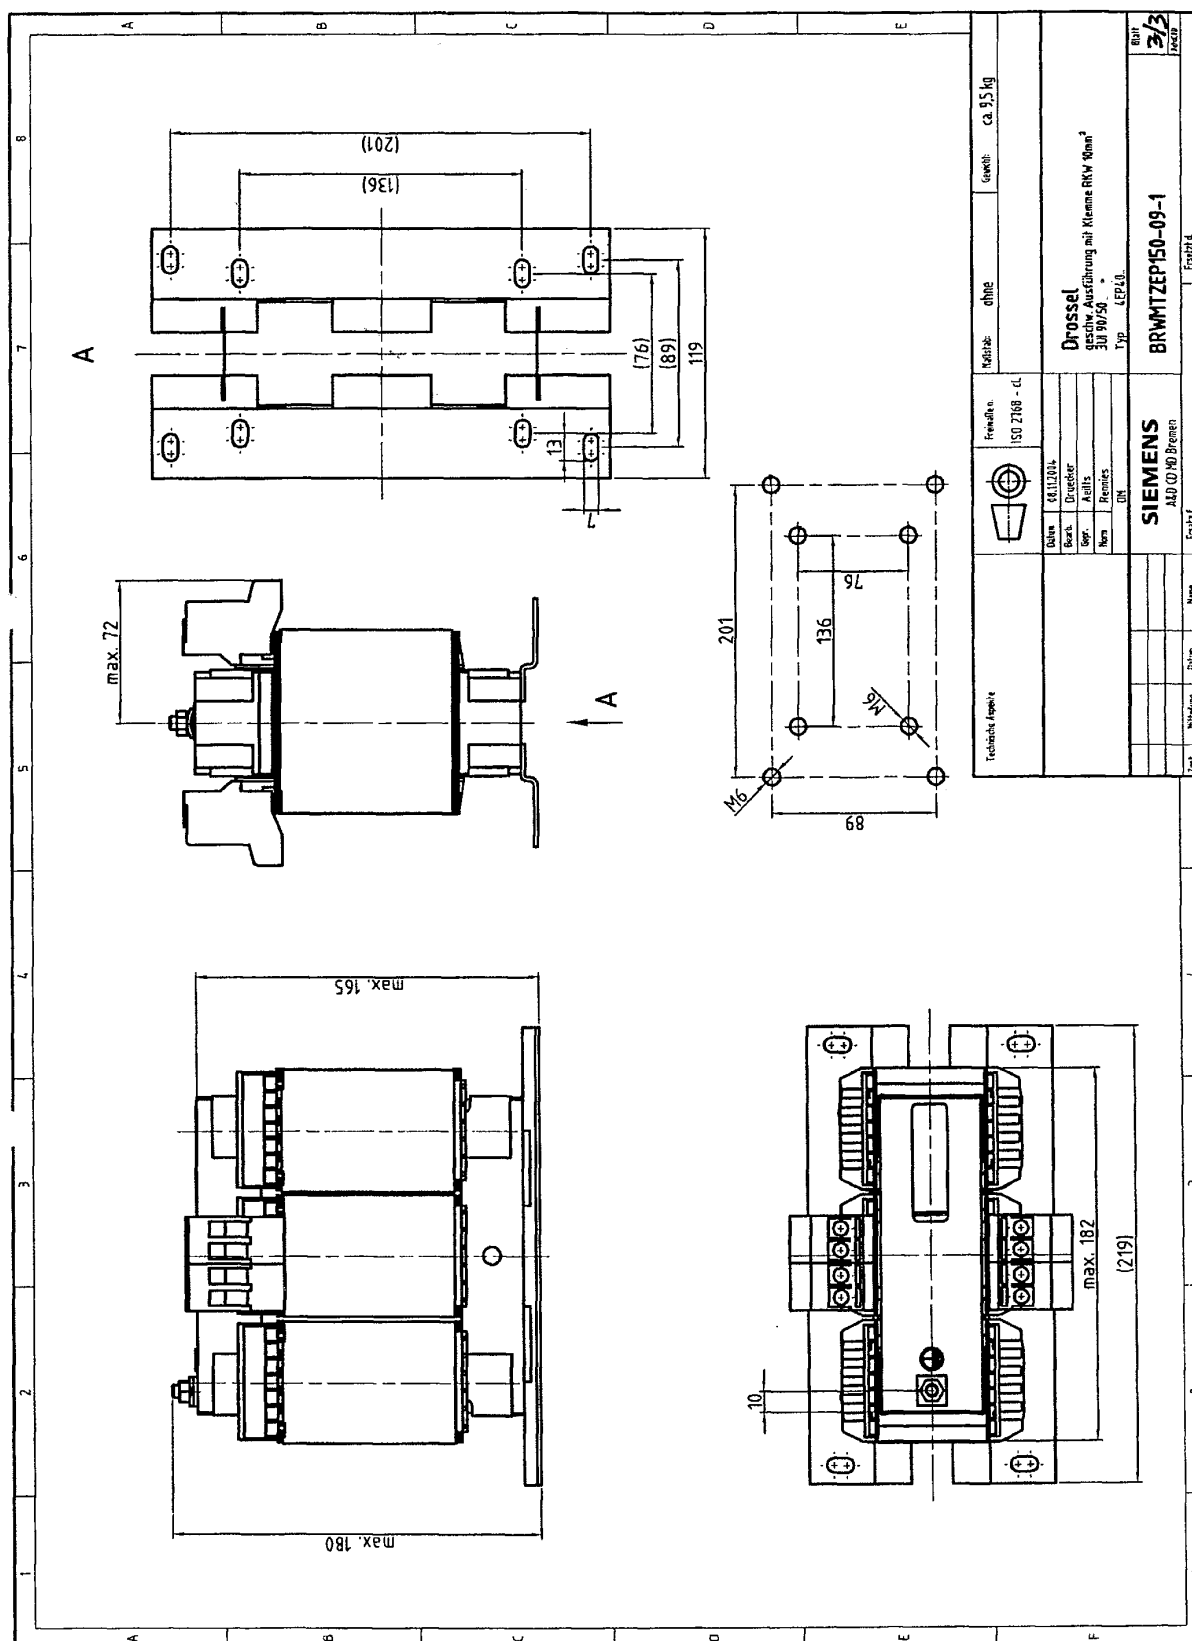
Disegno quotato della bobina di rete per Smart Line Module 16 kW
